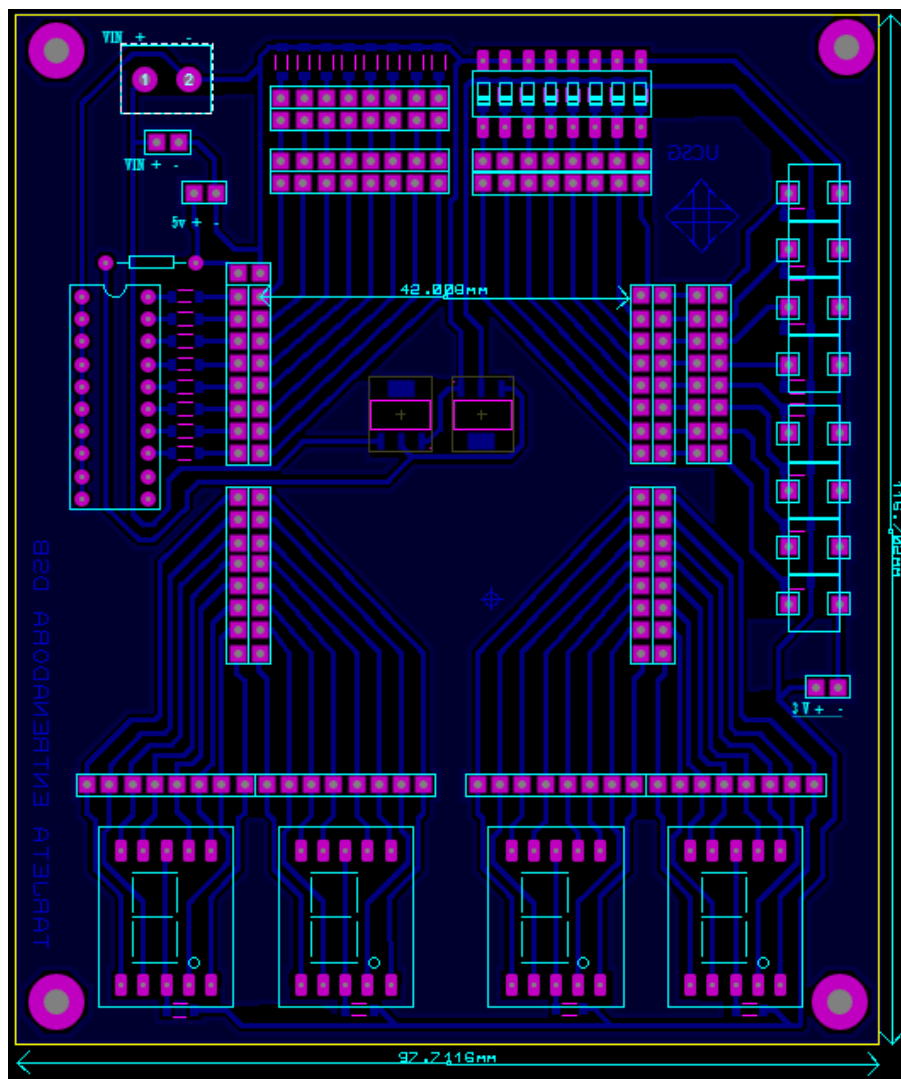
6: Diseño PCB de la placa entrenadora FPGA
